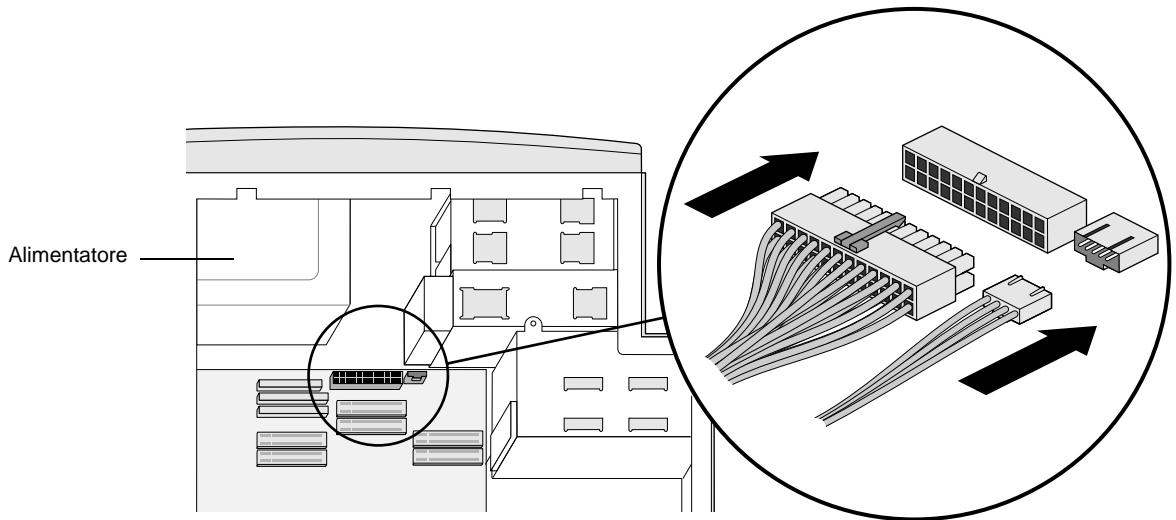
Collegamento dei cavi di alimentazione alla scheda di sistema
